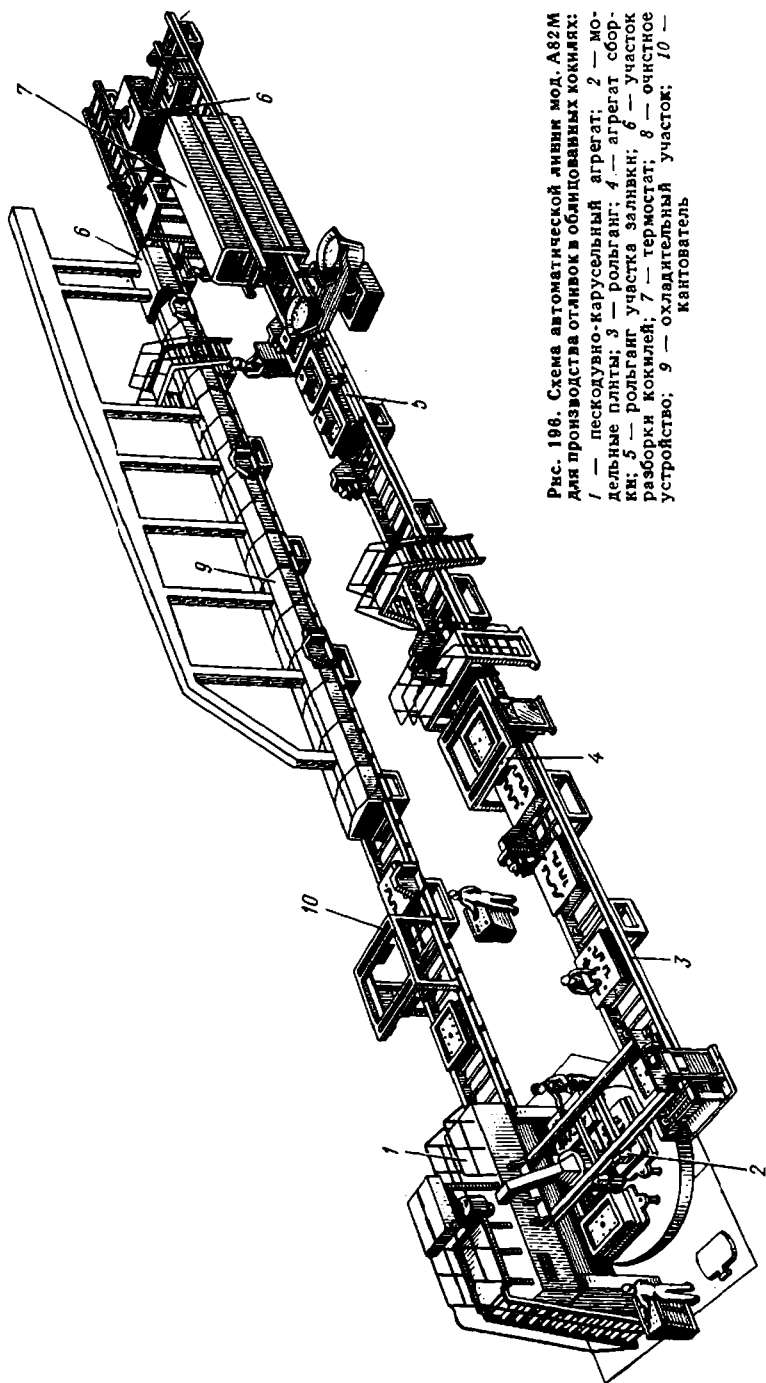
Схема автоматической линии мод. А82М для производства отливок в облицованных кокилах: 1 — пескодувно-карусельный агрегат; 2 — модельные плиты; 3 — рольганг; 4 — агрегат сборки; 5 — рольганг участка залвки; 6 — участок разборки кокилей; 7 — термостат; 8 — очистное устройство; 9 — охлаждаемый участок; 10 — кантователь
